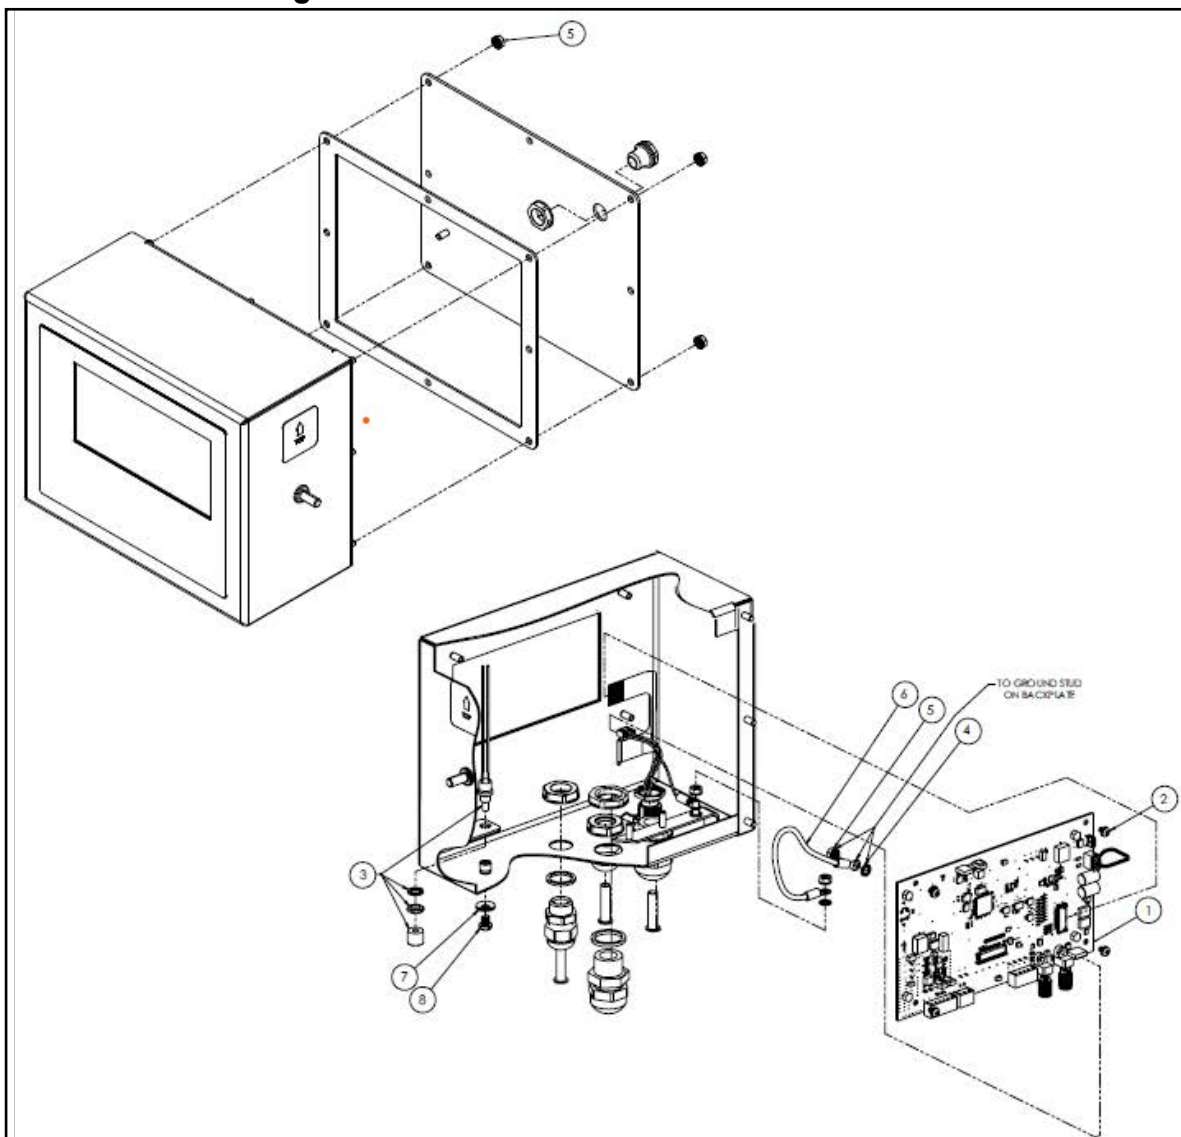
Vue éclatée des pièces de l'indicateur 882IS
